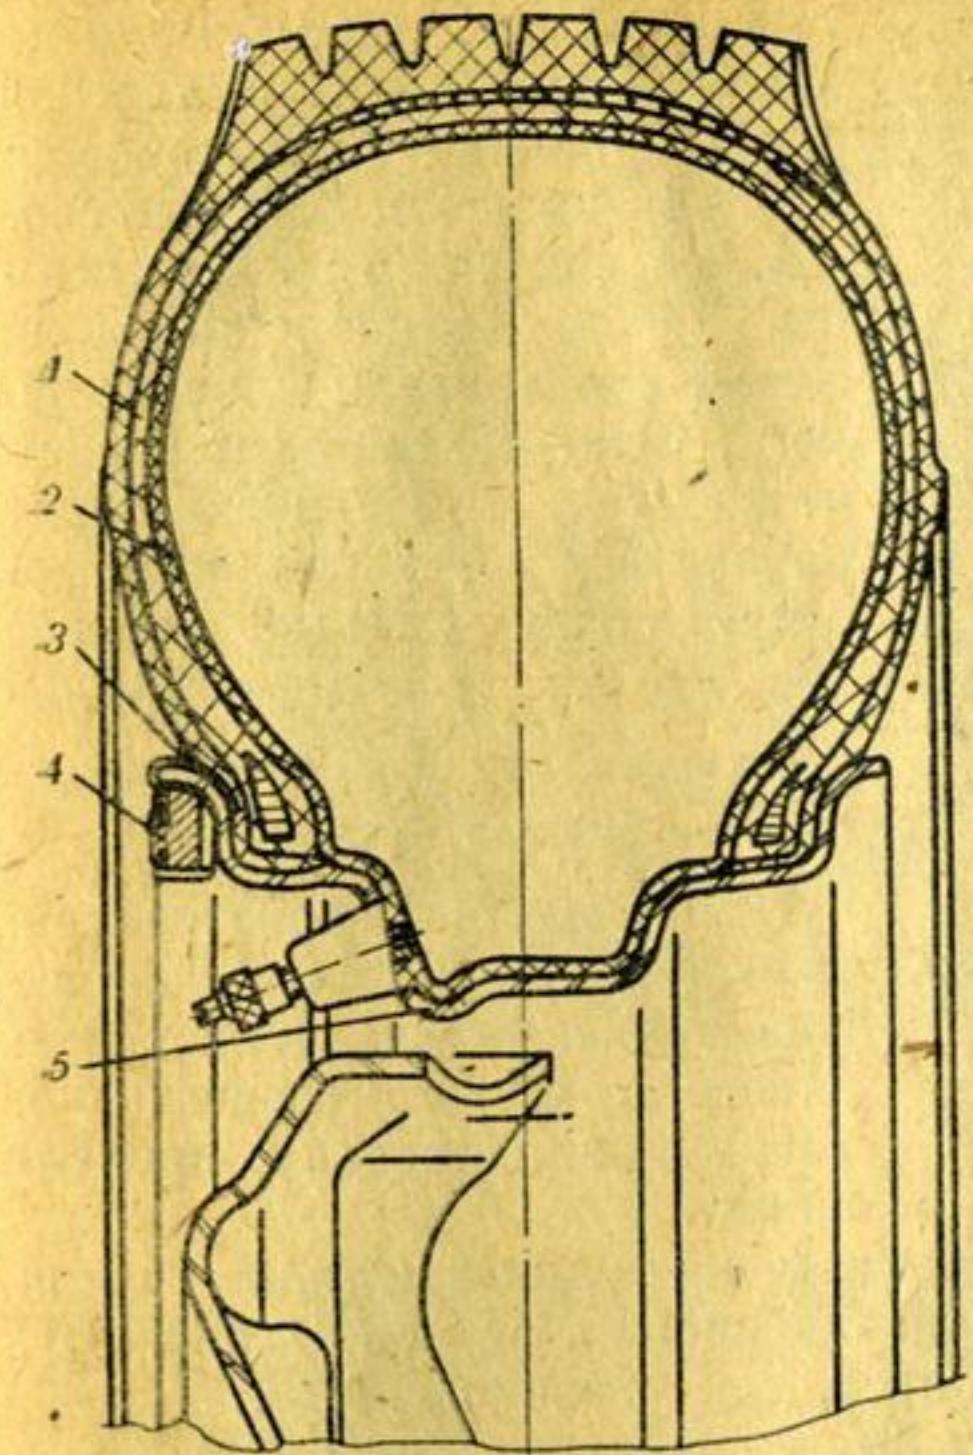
Крепление балансировочного грузика на ободе колеса:
